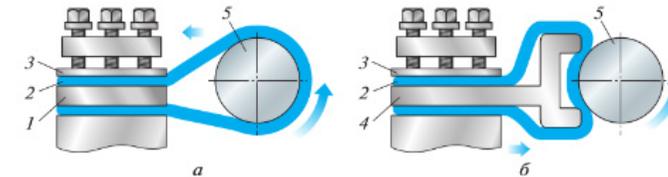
Полирование с помощью приспособлений: а — закрепление шлифовальной шкурки в резцедержателе; б — с применением «вилки» (1 — державка; 2 — шлифовальная шкурка; 3 — металлическая планка; 4 — «вилка»; 5 — изделие)
